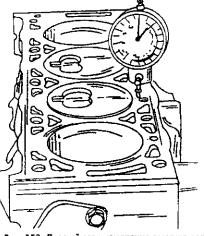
Первый этап измерения выступа поршия над поверхностью блока цилиндров.
